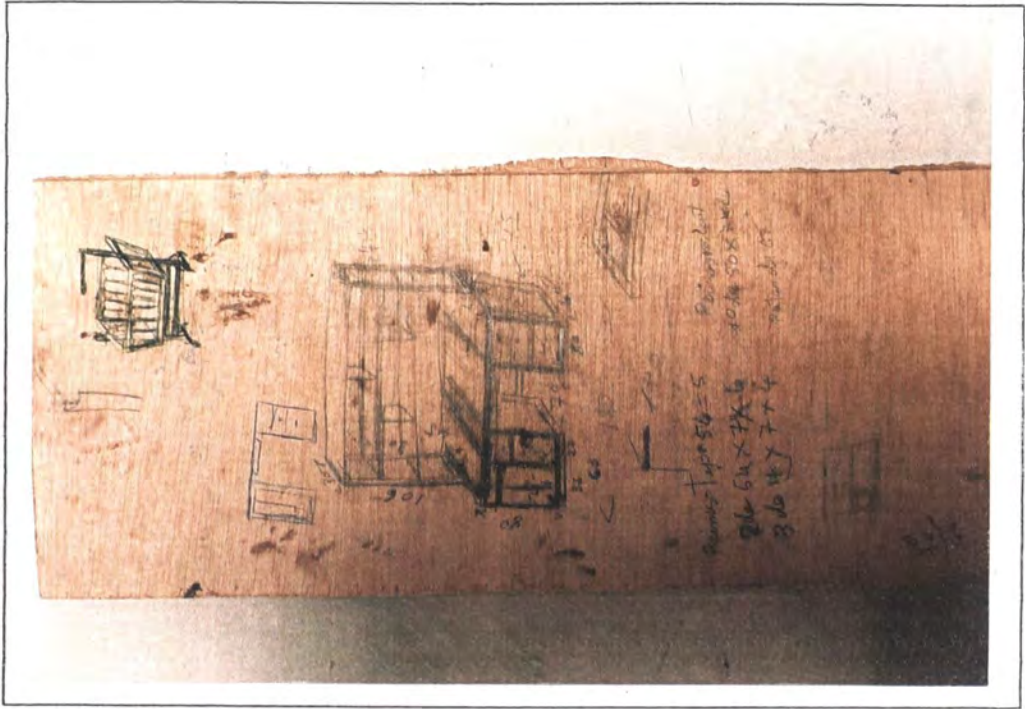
PLANO TECNICO / MUEBLES NOVEDADES
